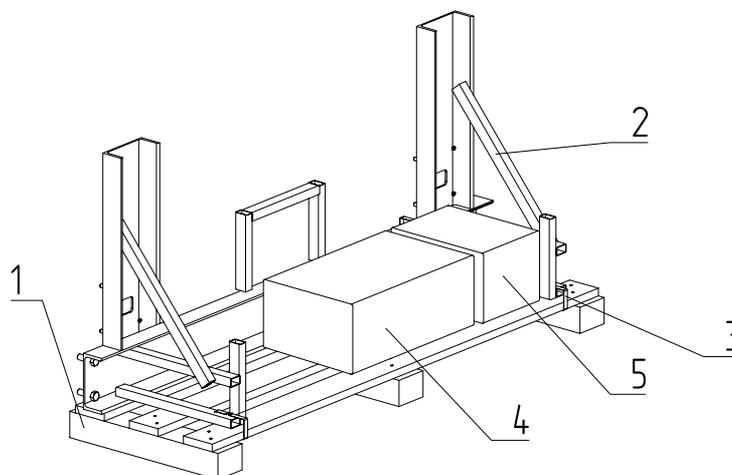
Упаковка рамы ворот опорной и коробок с комплектующими (FLGU.400.9801-03)
